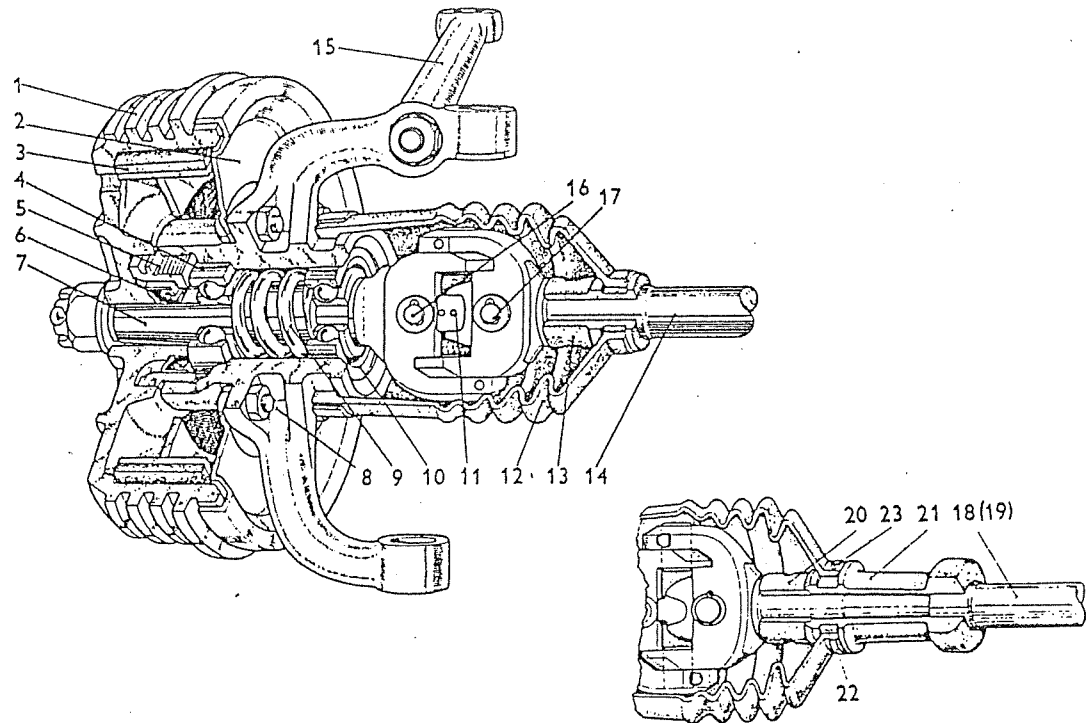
Framaxel och modifierad tätning (fr.o.m. ch.nr. 3967).
